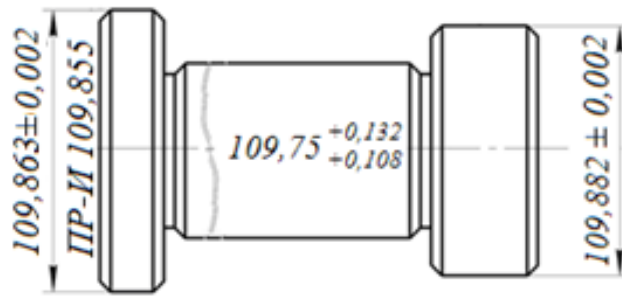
Эскиз калибра-пробки для контроля диаметров коренных опор двигателя ЯМЗ
